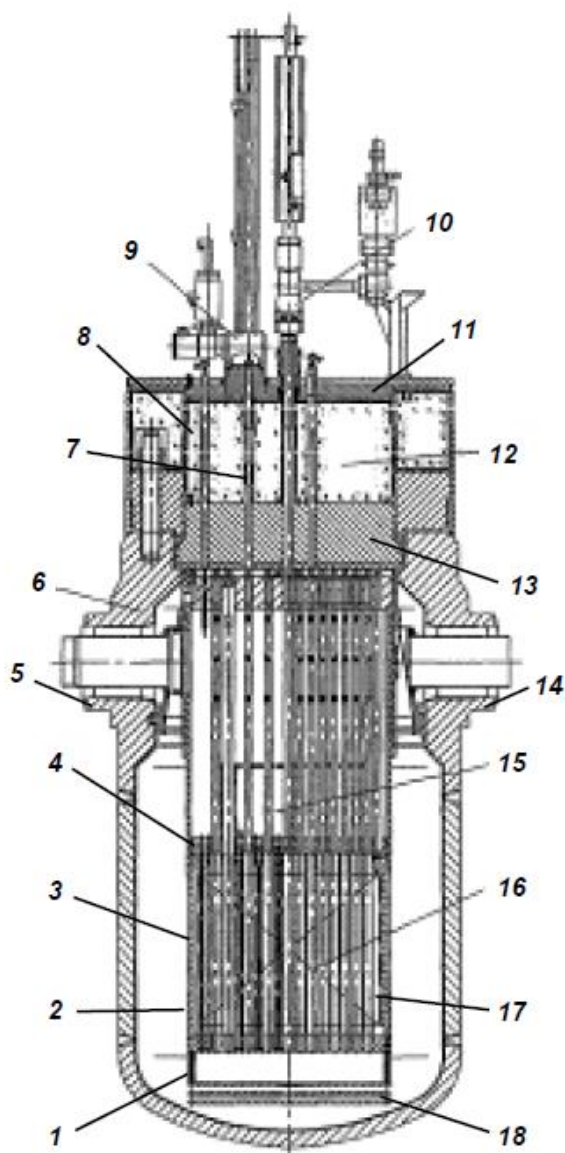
Реактор КЛТ-40С^[1]: 1 – щелевой фильтр; 2 – обечайка; 3 – пэл; 4 – РО КГ; 5 – патрубков парогенератора; 6 – корпус; 7 – стержни АЗ; 8 - биологическая защита; 9 – привод ИМ АЗ; 10 – привод ИМ КГ; 11 – верхняя плита; 12 – крышка; 13 – силовая плита; 14 – патрубков ЦНПК; 15 – выемной блок; 16 – активная зона; 17 - ТВС; 18 – донные экраны
